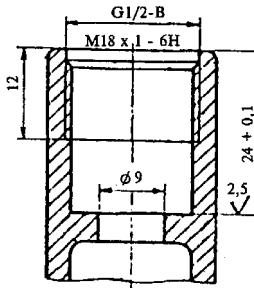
Основные размеры седла клапана и резьб для присоединения вентиляльных головок
